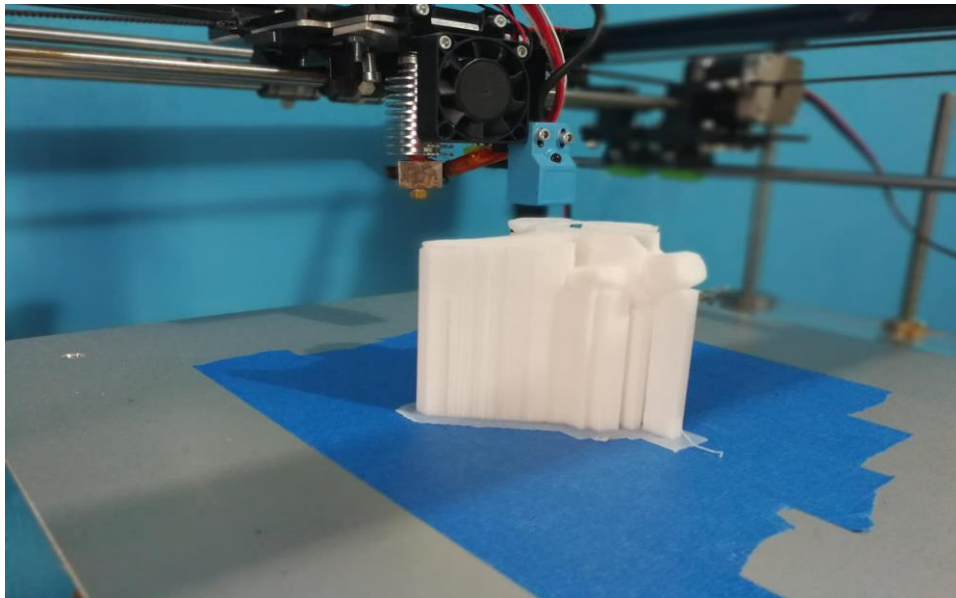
Vértebras impresas en PLA previo a el tratamiento impermeabilizante.
